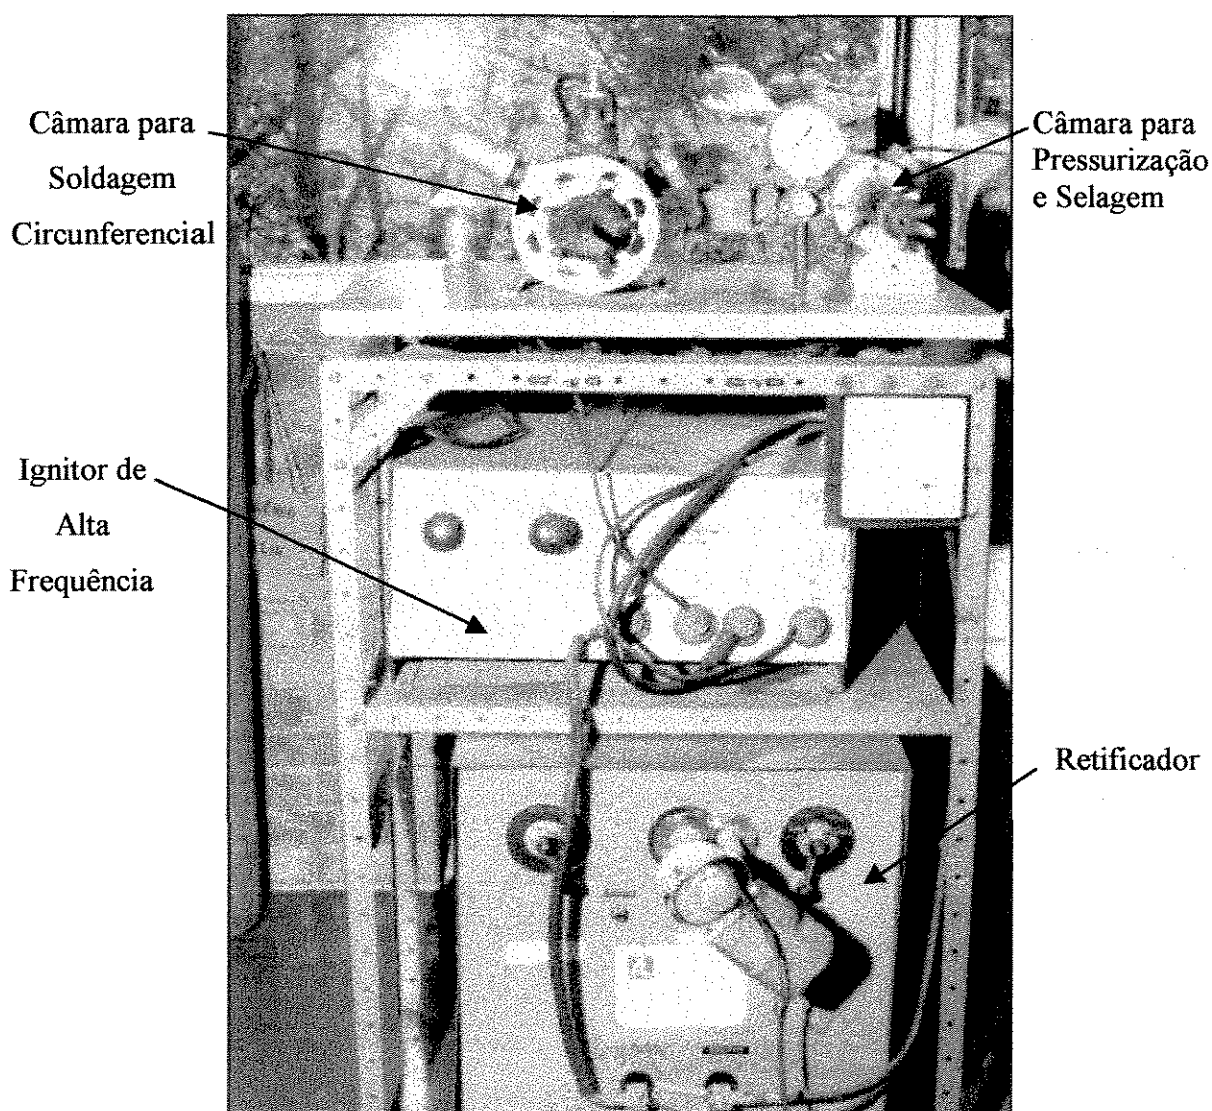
Máquina para soldagem, pressurização e selagem de varetas combustíveis.
